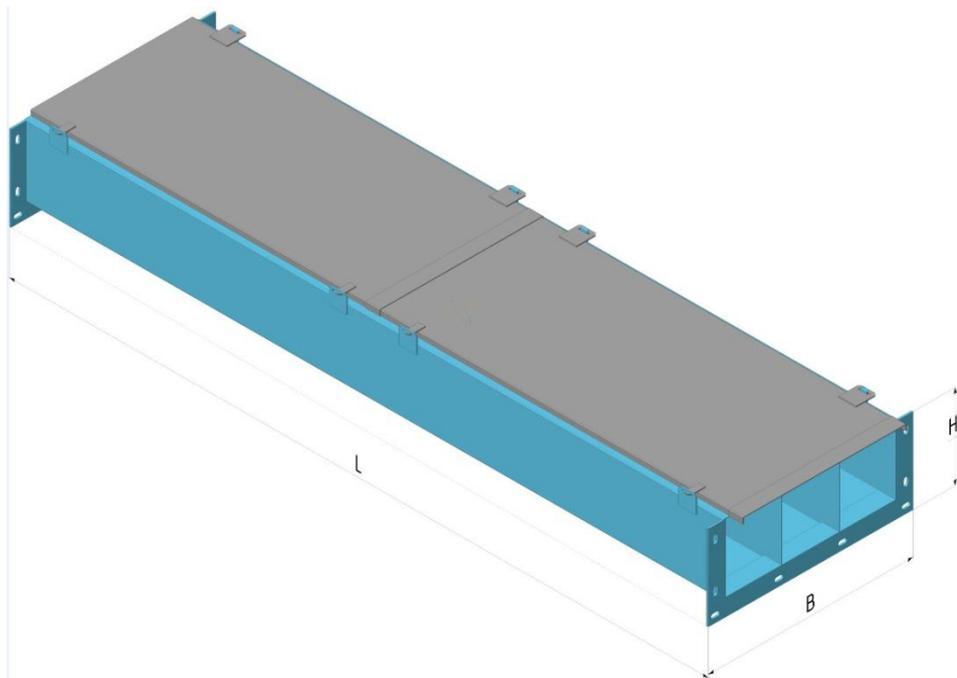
Короб кабельный блочный прямой плоский типа ККБ-ПО. Общий вид. Крышка с креплением на болты, две крышки длиной 1 м каждая.
